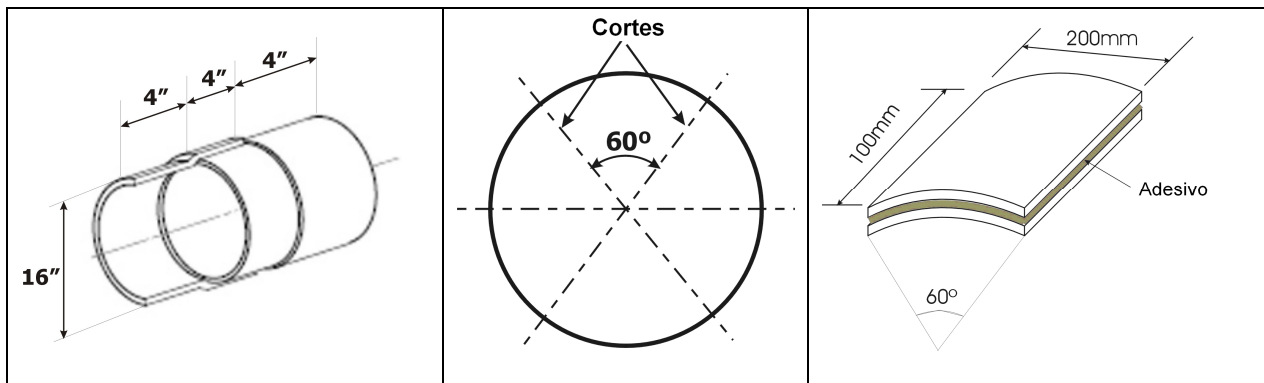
Dimensões e cortes dos dutos de 16 ".
